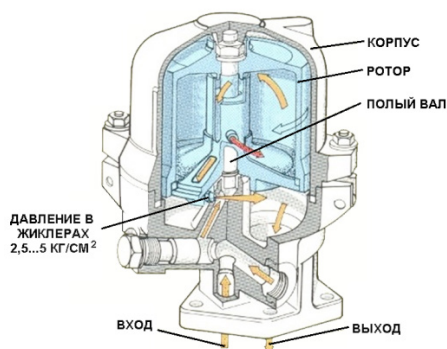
Центробежный фильтр; источник: Kraftfahrzeugtechnik TAK
